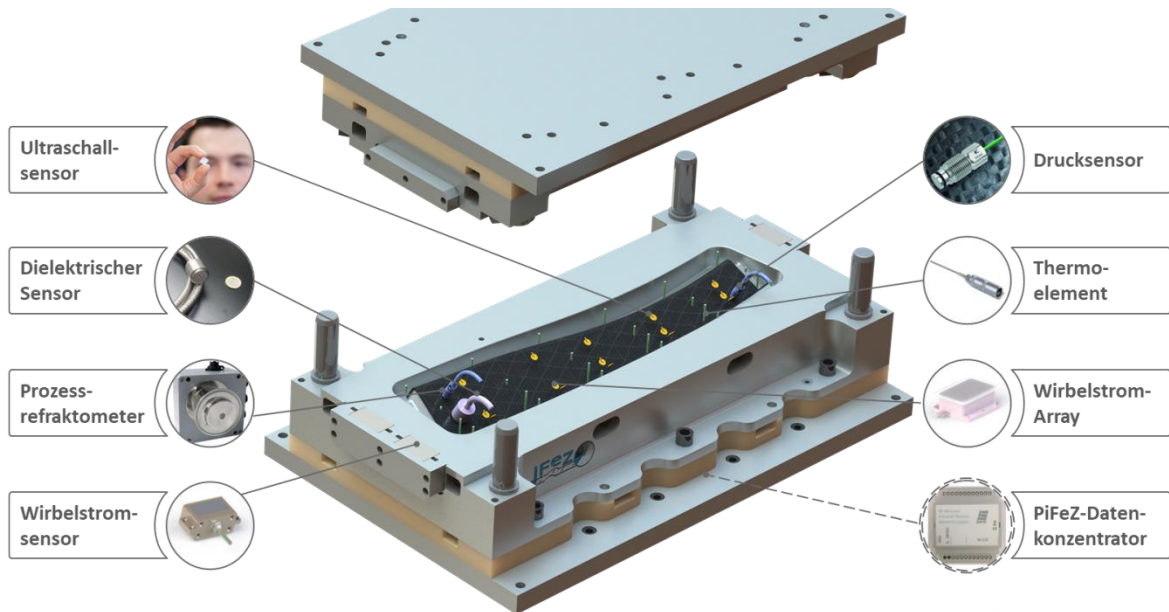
Virtuelles Abbild der Sensorintegration für das "intelligente Formwerkzeug der Zukunft"
